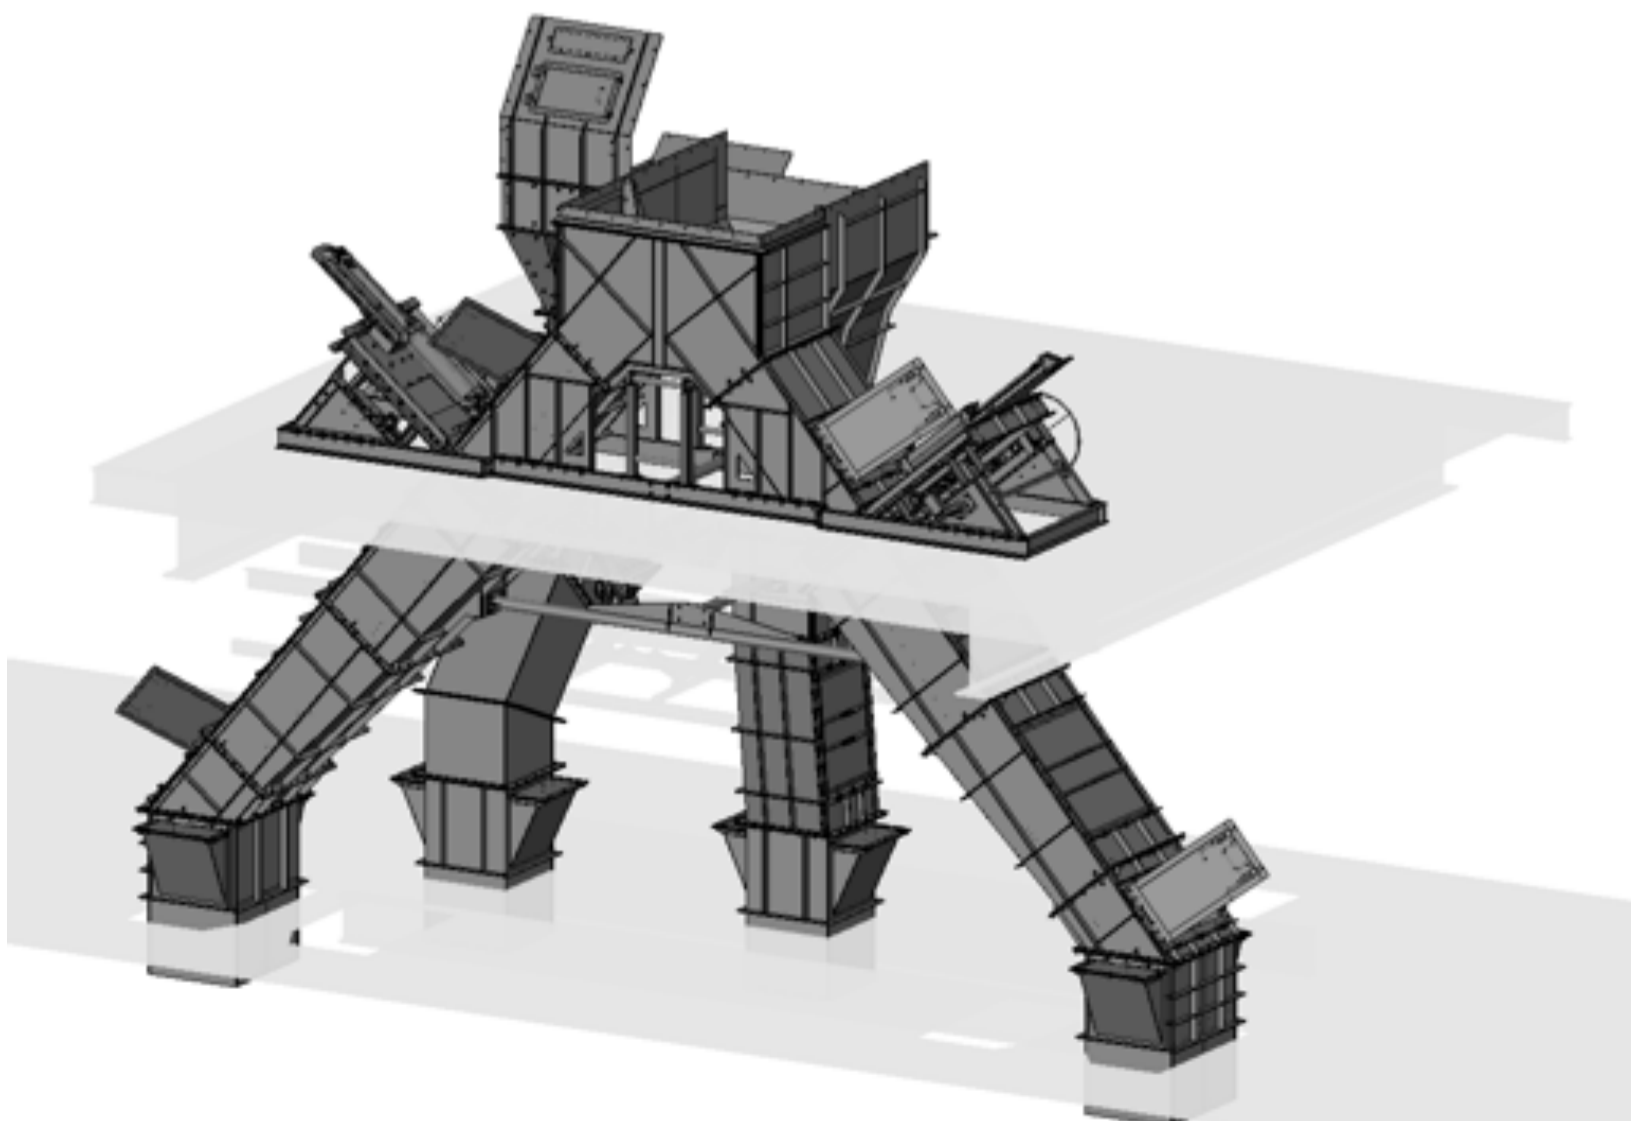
Widok jednej sekcji zaprojektowanej konstrukcji zabudowy podajników i przesiewaczy wibracyjnych
